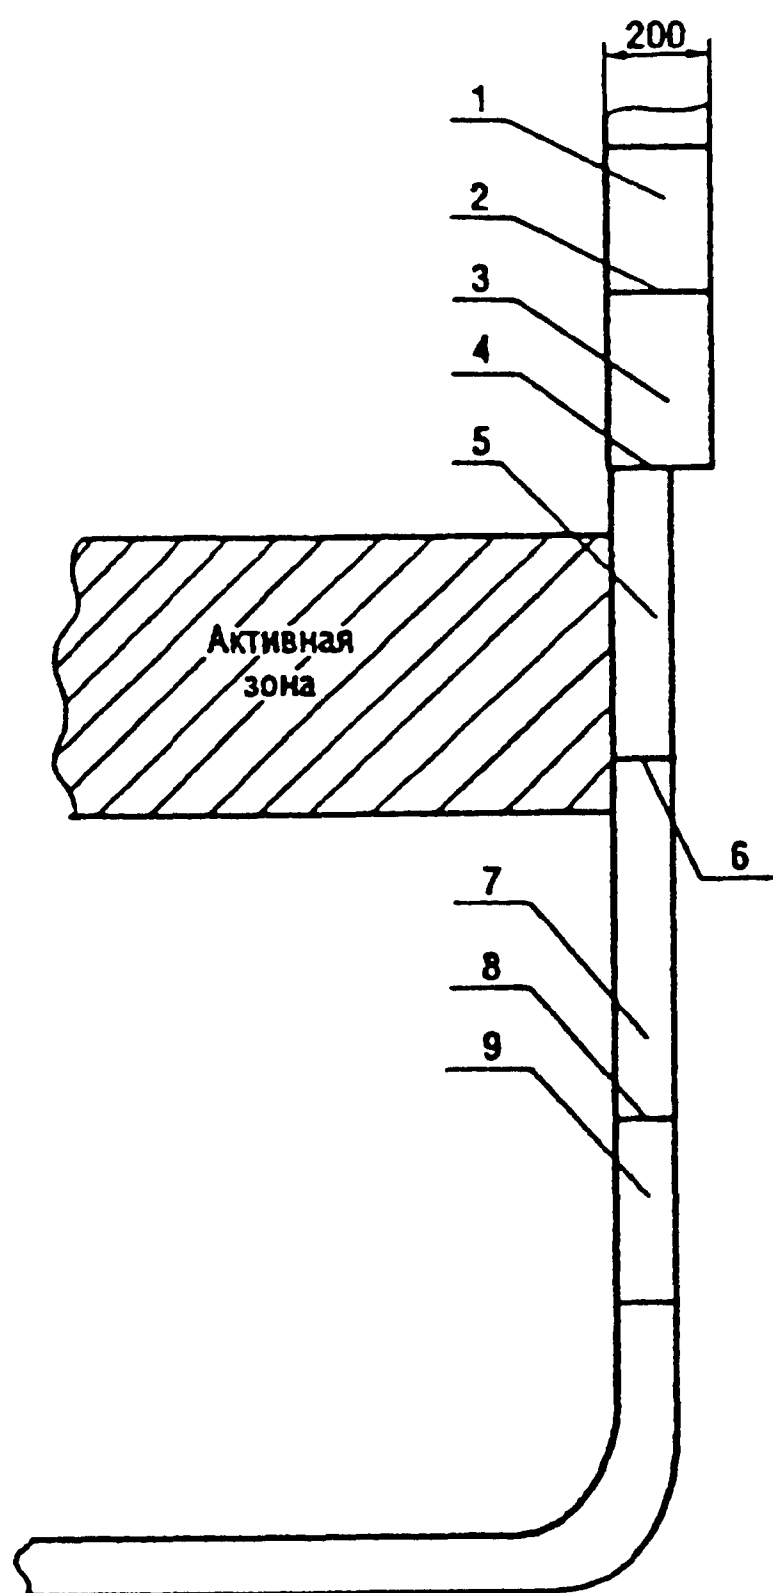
Схема расположения сварных швов и обечайек КР II блока КолАЭС (к рис. 38):
